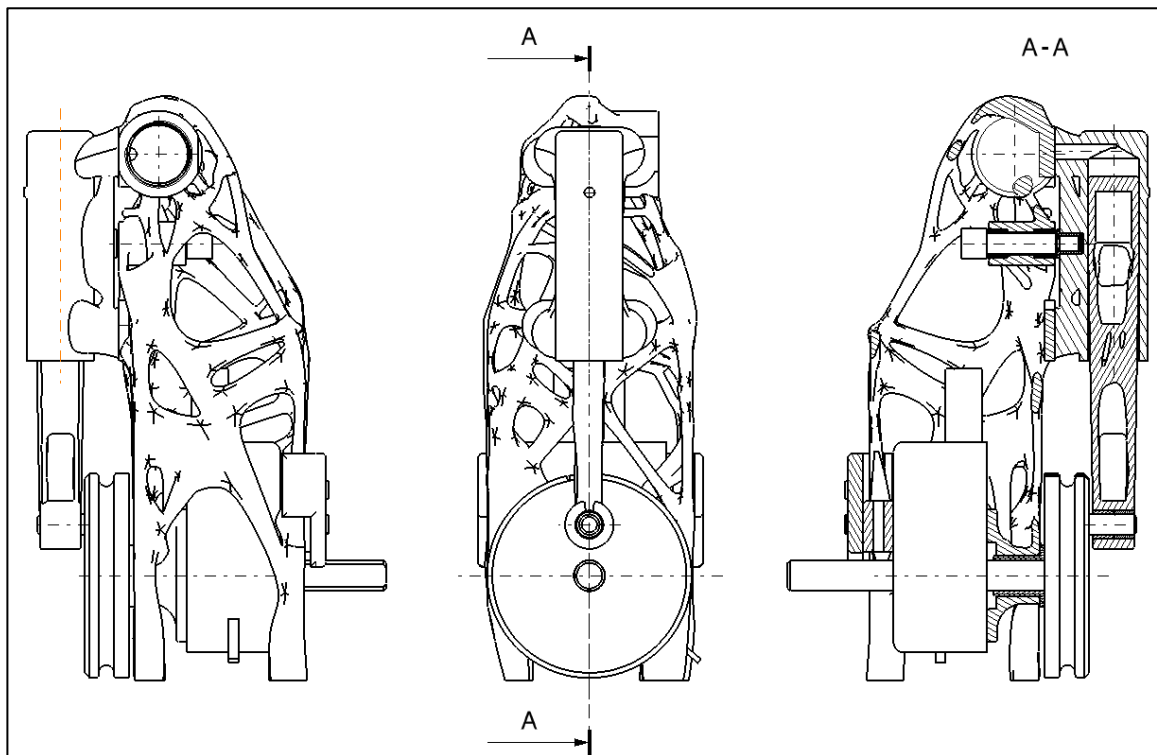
Extrait du dessin d'ensemble du moteur Eam1 de l'étude de cas « moteur à air »
